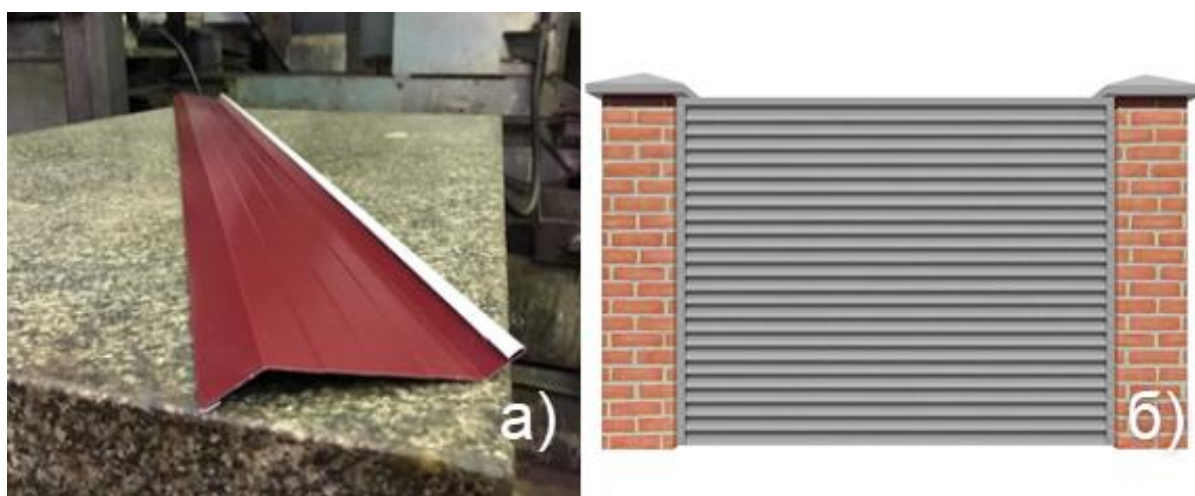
Забор-жалюзи из зетовых ламелей а) Профиль; б) Конструкция сборки
